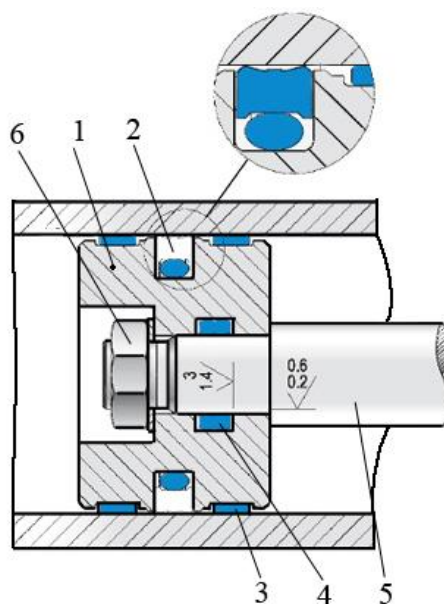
Поршневой узел современного гидроцилиндра с опорными кольцами из полиамидного композита [6]: 1- поршень; 2- уплотнение поршня; 3- опорные кольца; 4- кольца резиновые; 5-шток; 6-гайка
